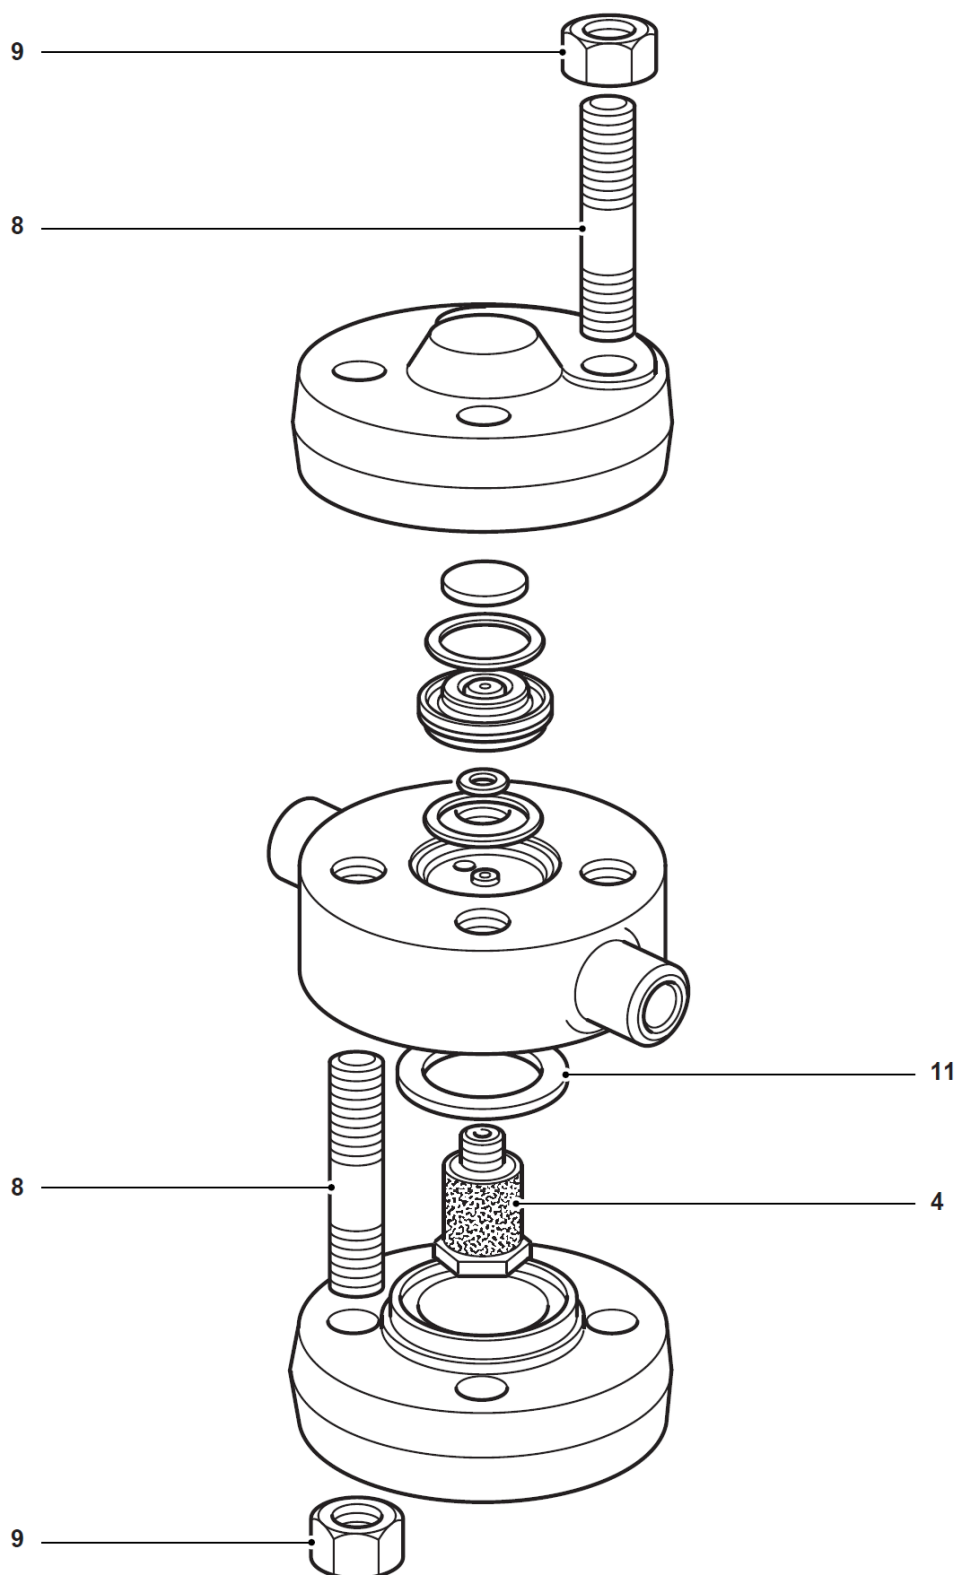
TD120M avec des raccords à souder butt weld
